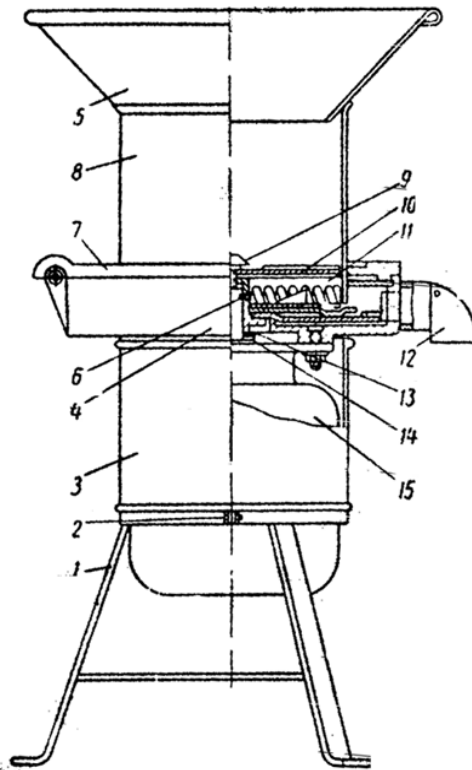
Коренерізка КПІ-4: 1-рама; 2-стяжний болт; 3-кожух; 4-корпус камери подрібнення; 5-завантажувальна горловина; 6-штифт; 7-кришка камери подрібнення; 8-бункер; 9-спеціальний болт; 10-верхній диск; 11-дека з зубами; 12-вивантажувальний рукав; 13-гумовий сальник; 14-регулювальні кільця; 15-електродвигун.
